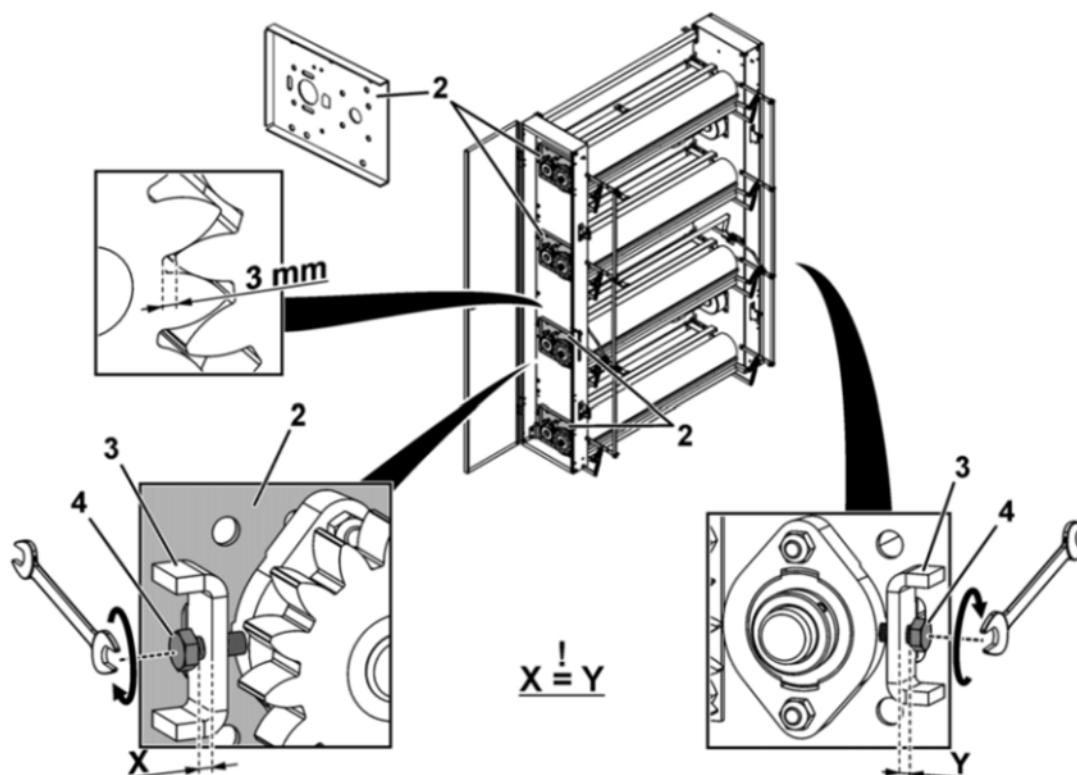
Зубчатые колёса прижимного ролика привода помётоуборочной ленты
